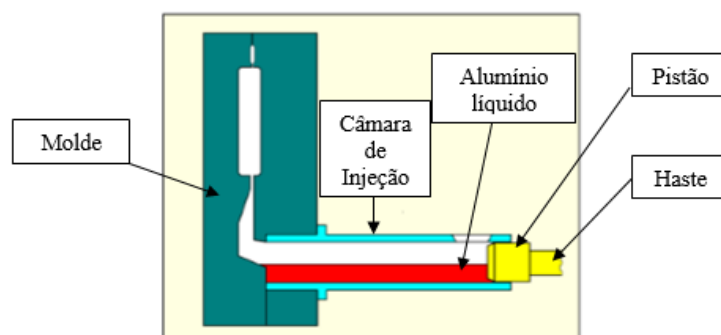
O conjunto de injeção de alumínio sob pressão.
